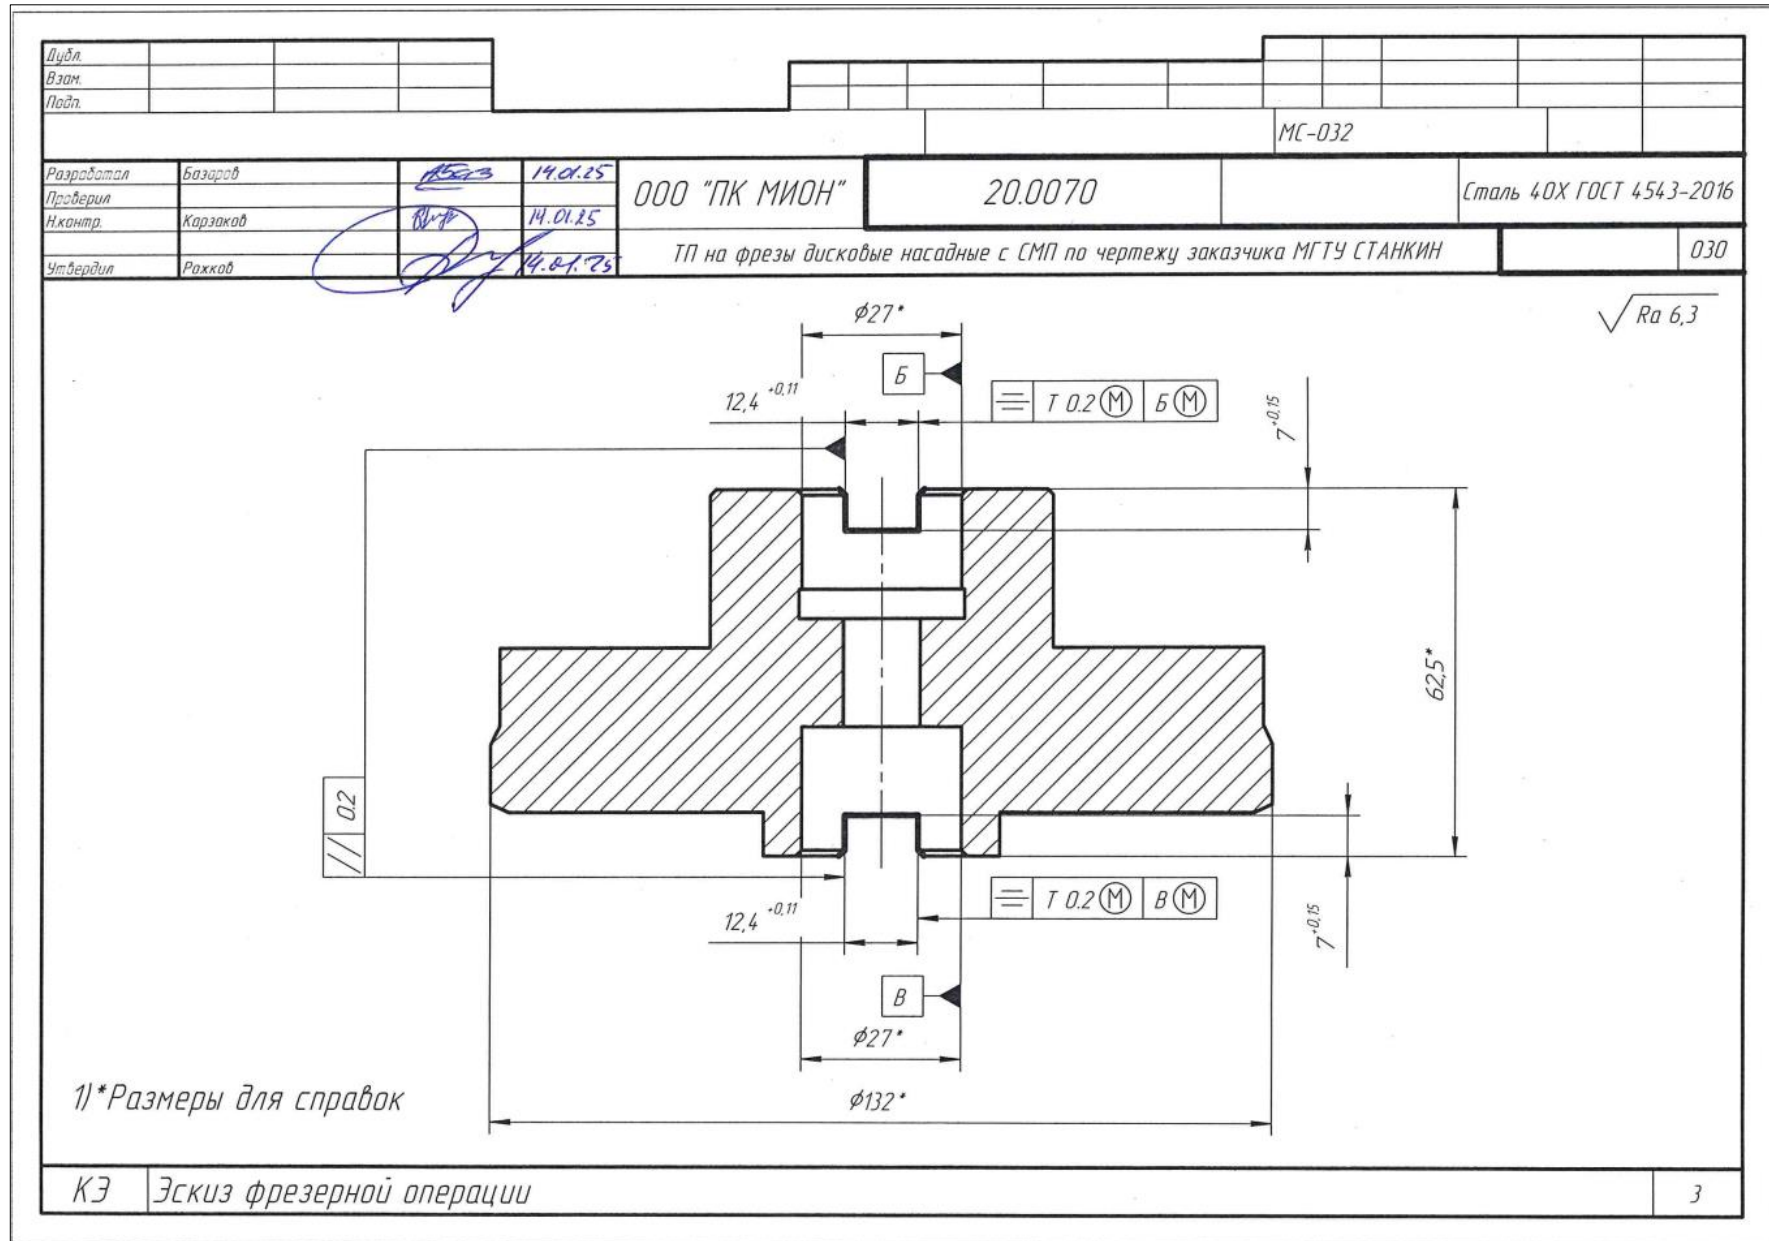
Эскиз фрезерной операции для формирования шпоночных пазов.
